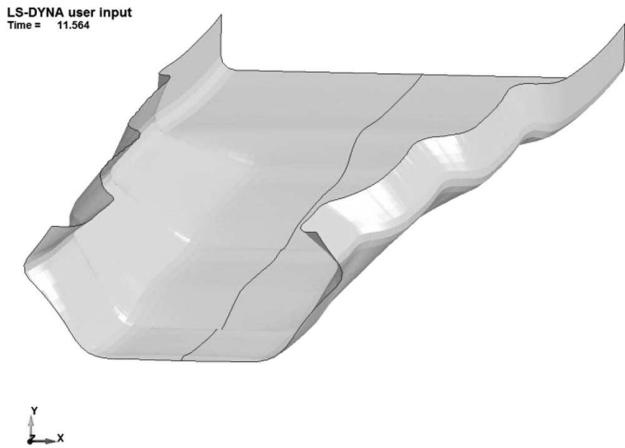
Заготовка 80×40×4 мм с отогнутыми краями после формовки
